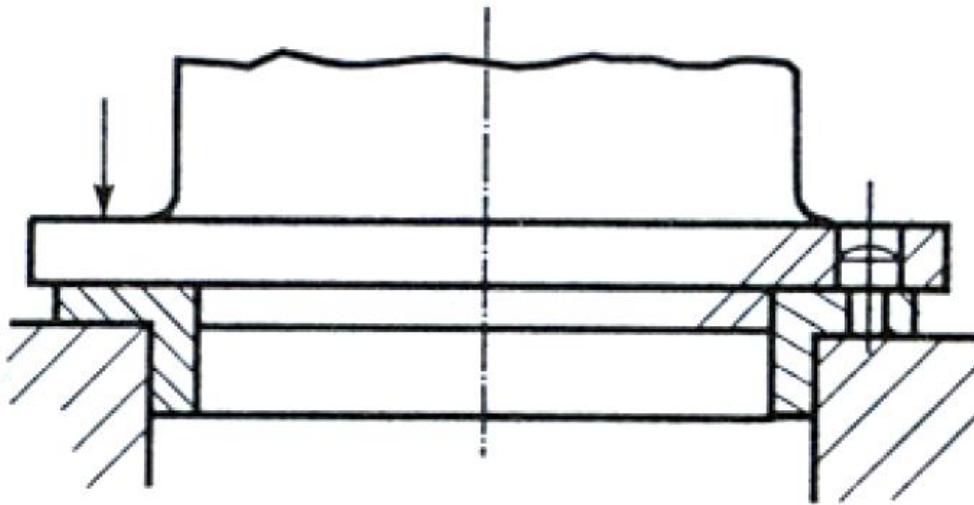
Схема базирования деталей фланцевого типа
